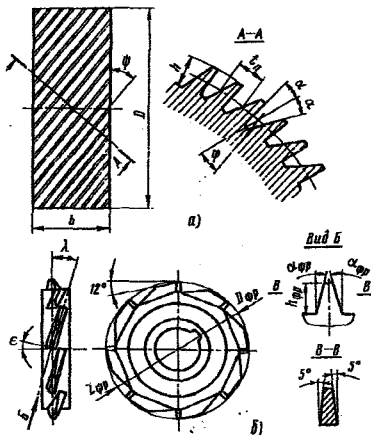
Конструкция винтового лабиринта (а) и дисковой фрезы определенной установки (б)
